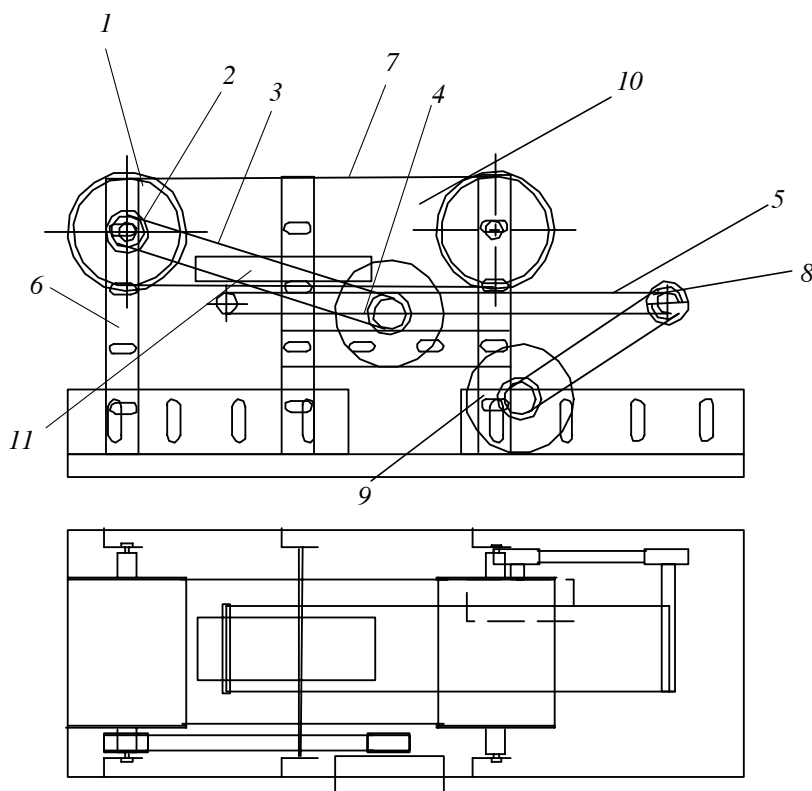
Эскиз магнитного сепаратора: 1 – приводной барабан верхнего конвейера; 2 – шкив; 3 – ремень; 4 – верхний реверсивный двигатель РД-09; 5 – нижний конвейер; 6 – оцинкованные пластины; 7 – лента; 8 – приводной барабан нижнего конвейера; 9 – нижний реверсивный двигатель РД-09; 10 – верхний конвейер; 11 – короб с магнитами
